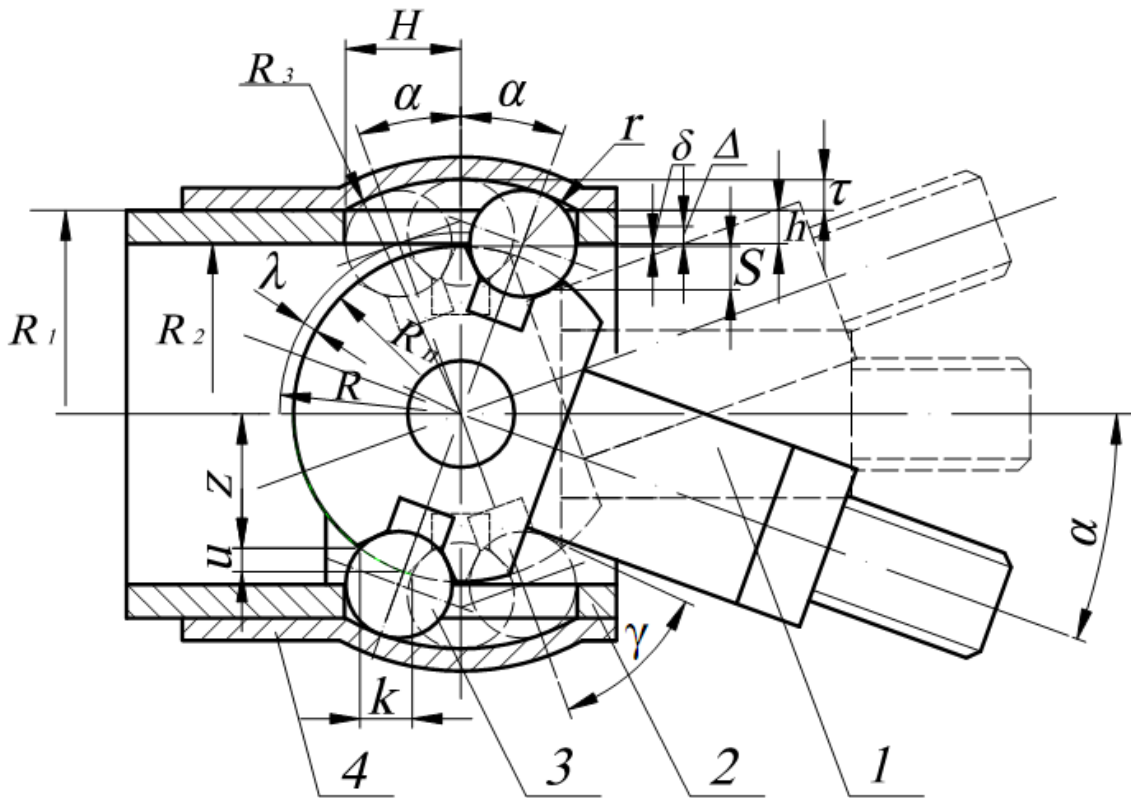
Розрахункова схема конструкції шарнірного з'єднання гвинтового робочого органу
